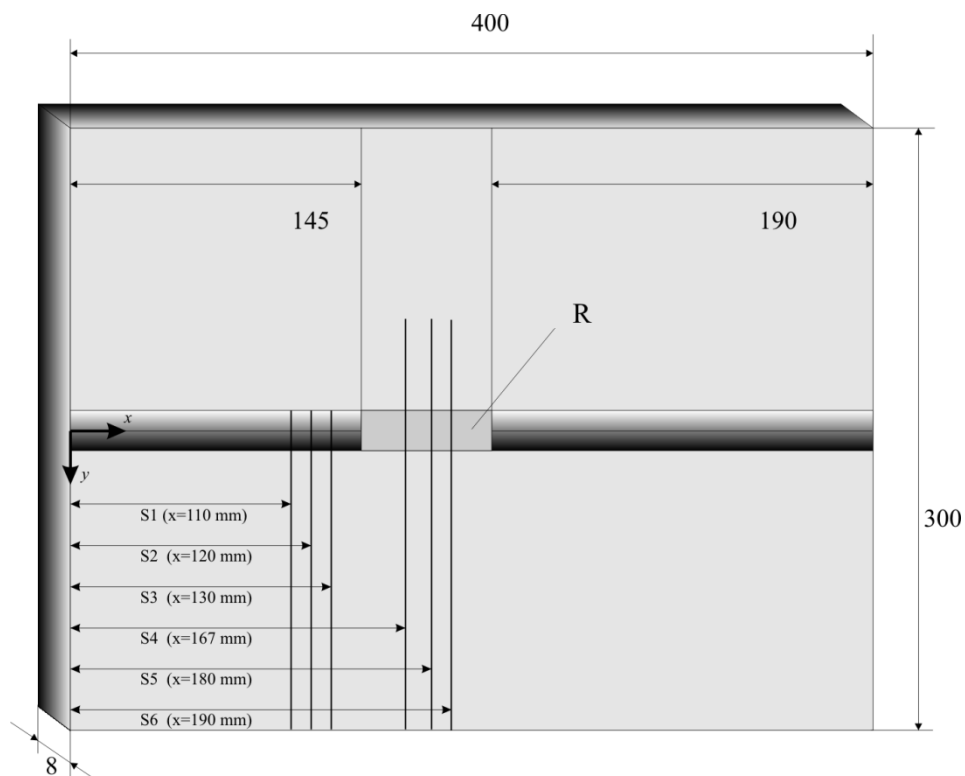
Схема зварного зразка зі сплаву АМг5: S1-S6 - перерізи, в яких визначалися залишкові напруження, R - область, в якій видалено посилення зварного шва.
